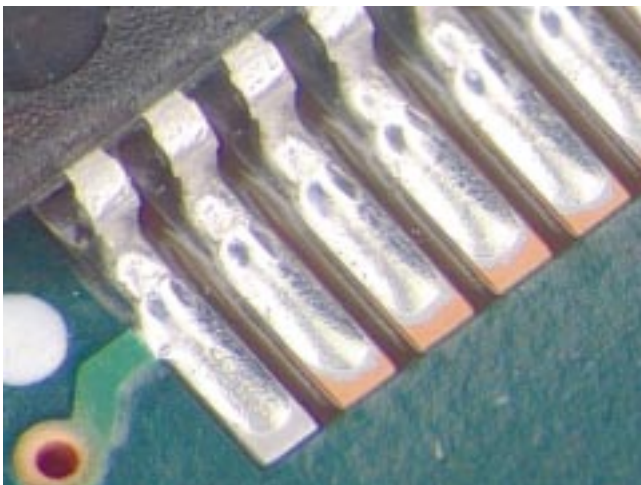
Soldadura SnPb; Flux Soluble en Agua
